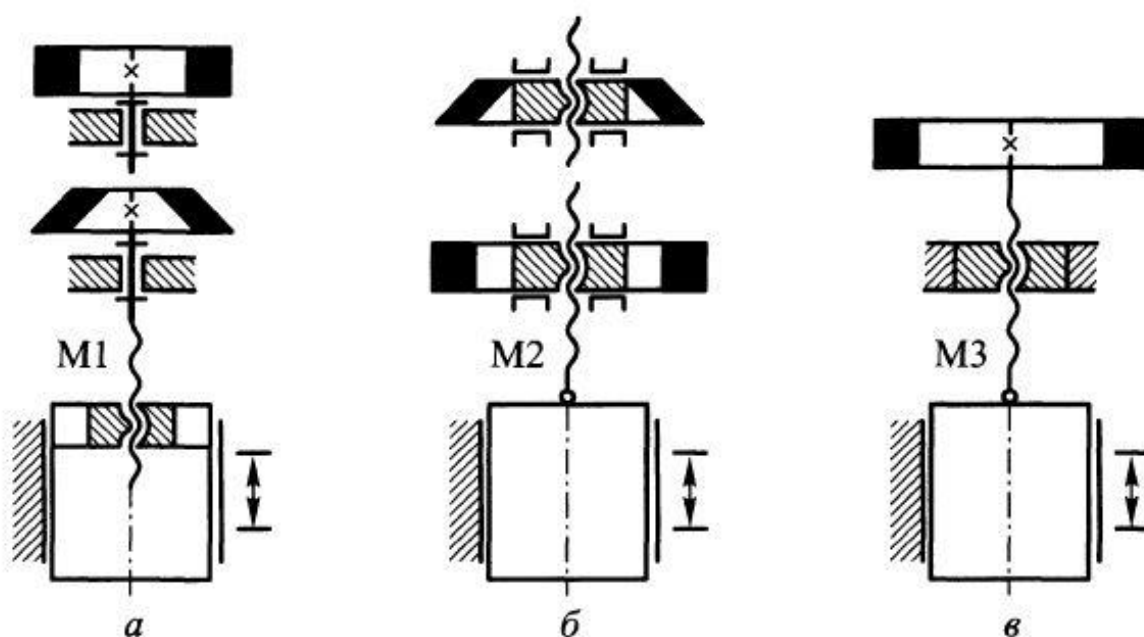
Исполнительные механизмы винтового пресса
